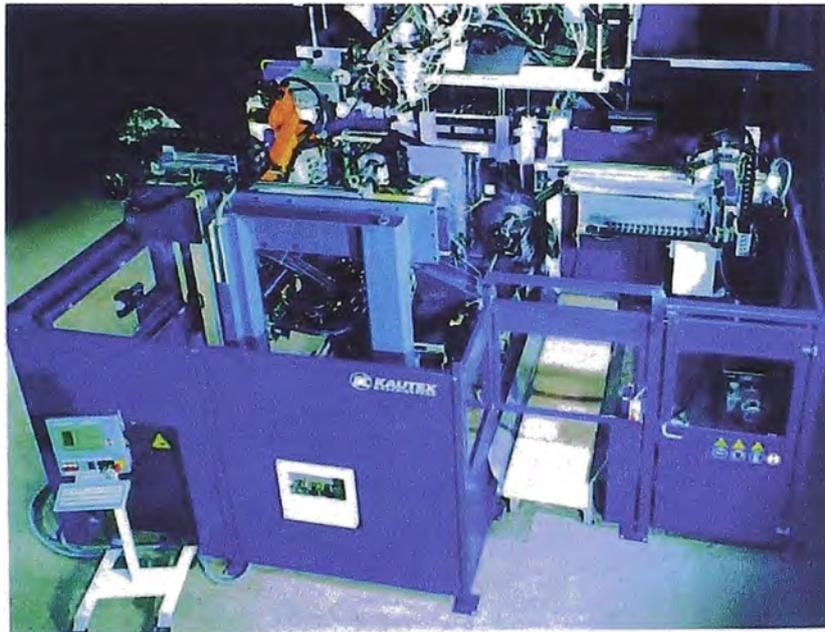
MAQUINA SOPLADORA (EXTRUSIÓN – SOPLADO)
